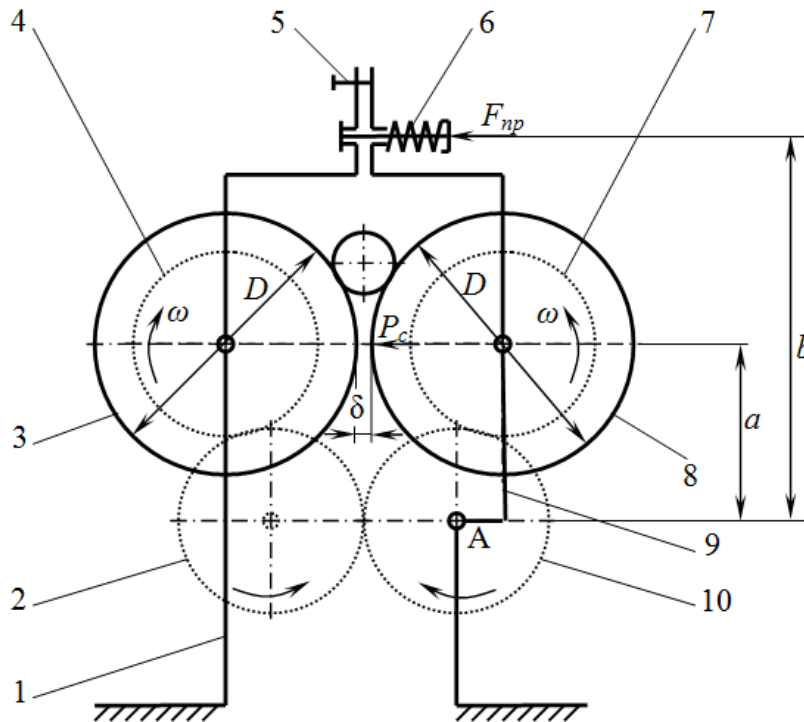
Схема вальцьового плющильного робочого органа: 1 – нерухома стійка; 2, 10 – проміжні шестерні; 3 – ведучий валок; 4 – шестерня ведучого валка; 5 – регулювальний гвинт; 6 – пружина; 7 – шестерня веденого валка; 8 – ведений валок; 9 – рухома стійка.
